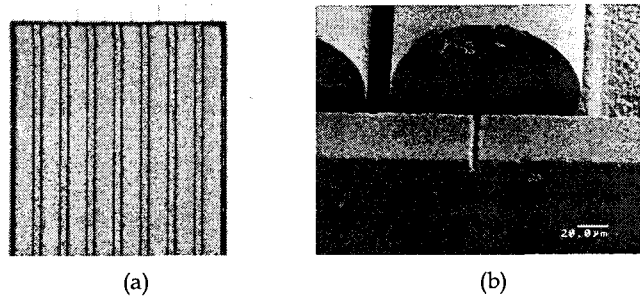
가공된 mold master(a) 및 광섬유가 정렬된 mold master(b).
